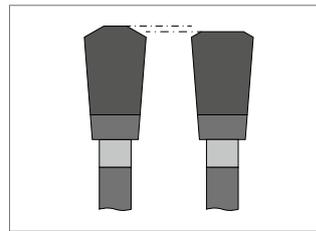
Disco plano trapezoidal (TR-F-Fa)
